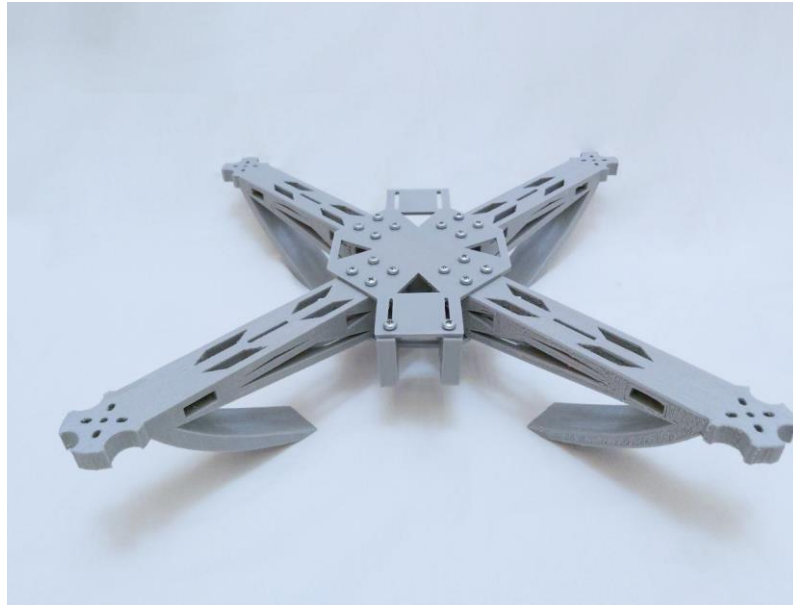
Ensamblaje de Piezas Impresas en 3D Utilizando PETG
